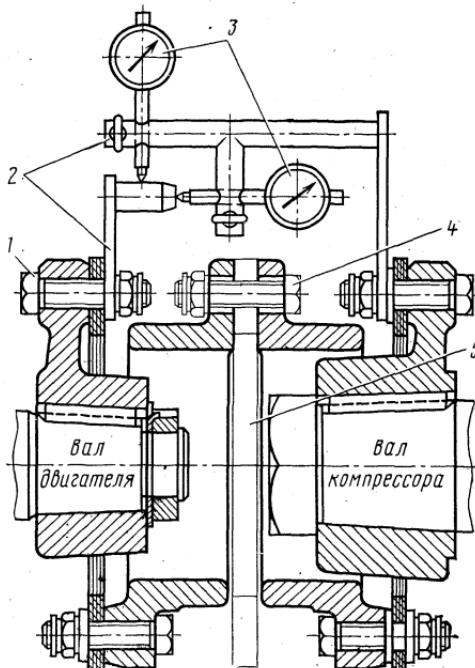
Приспособление для центровки валов двигателя НБ-431А и компрессора
